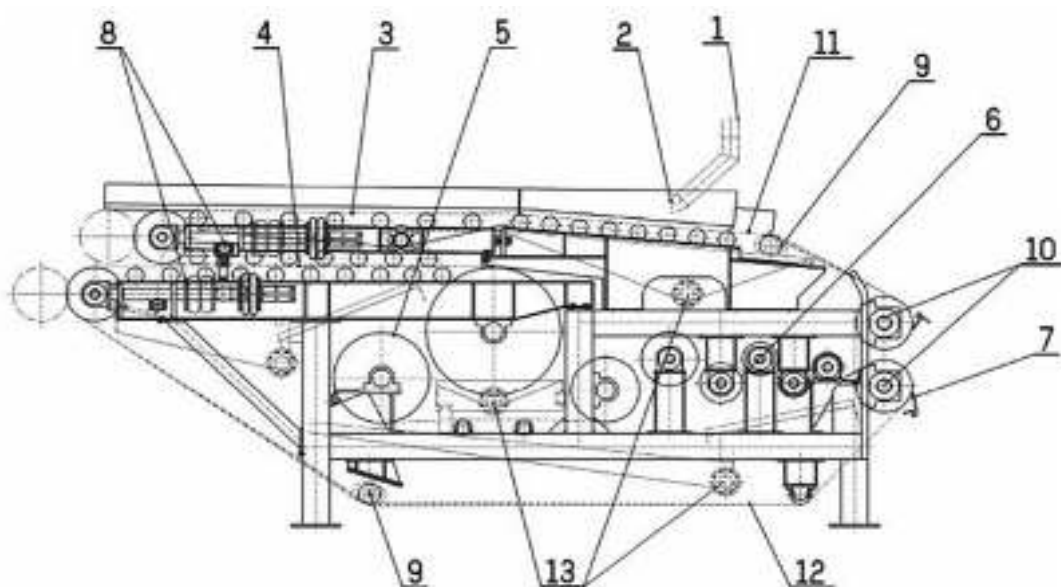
Устройство ленточного фильтр-пресса CPF 2200 S8: 1 – подача осадка; 2- загрузка осадка; 3 – зона предварительного обезвоживания; 4 – клиновидная зона; 5 – зона предварительного прессования; 6 – зона высокого давления; 7 – сброс кека; 8 – натяжение ленты; 9 – регулировка ленты; 10 – привод; 11 – верхняя лента; 12 – нижняя лента; 13 – слив фильтрата
